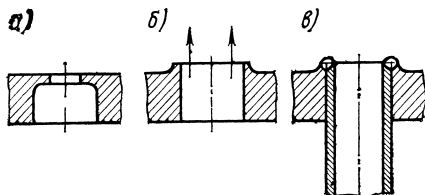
Вариант выполнения соединения труб с трубной доской: а — сверление; б — выштамповка отбортовки; в — сварка
